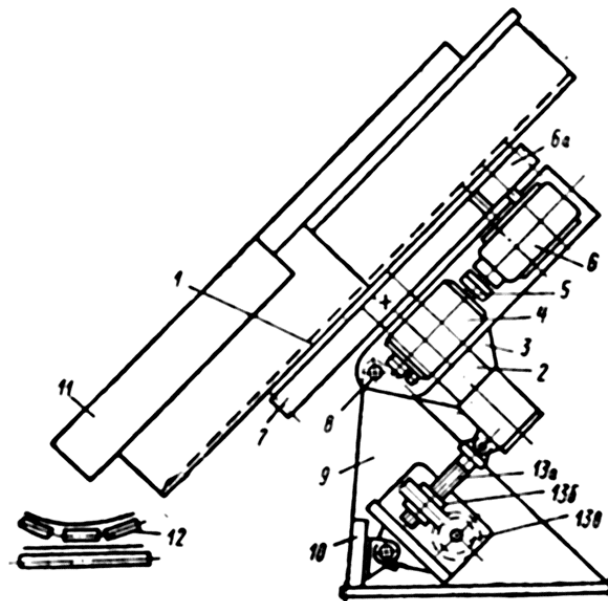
Механізми обертання і нахилу чаші чашевого гранулятора: 1 – чаша; 2 – вісь, що обертається; 3 – опора; 4 – електродвигун постійного струму; 5 – муфта; 6 – конічно-циліндровий редуктор; 6а – шестерня; 7 – зубчатий вінець; 8 – валки; 9 – дві стійки; 10 – поперечна балка; 11 – лоток; 12 – конвеєр; 13 а – тяга-гвинт; 13 б – тяга гвинтова пара; 13 в – черв'ячна передача.
